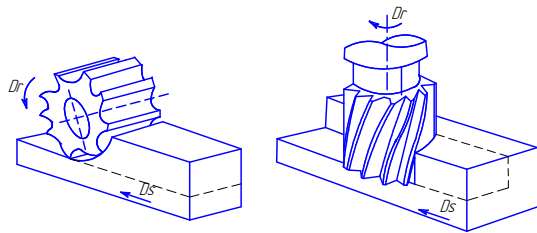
Кінематичні схеми периферійного та комбінованого фрезерування
